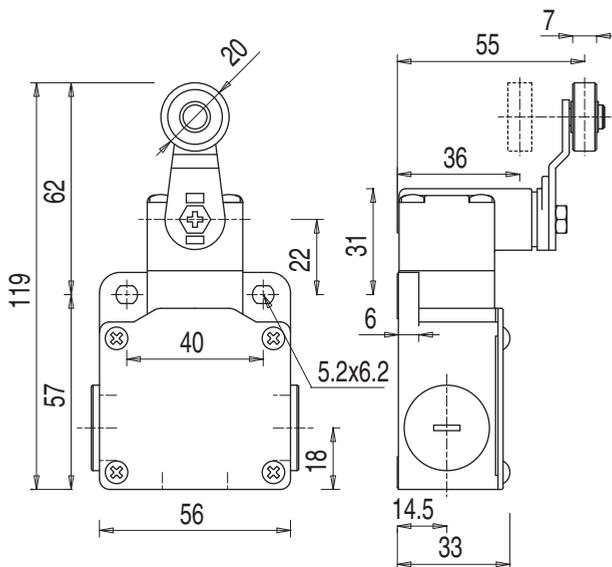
Dimensões do S300-M0C3-M20-31 / S300-M13C3-M20-31 em mm
